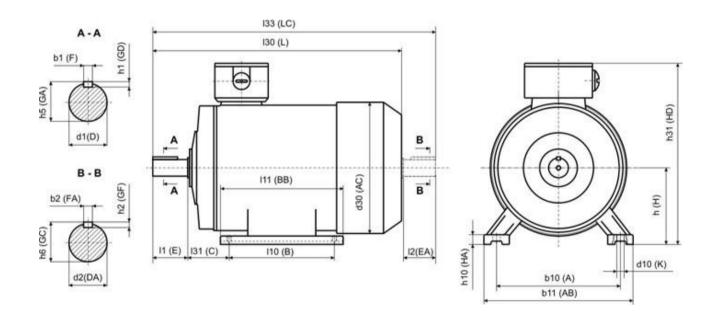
габаритный чертеж электродвигателя исполнение ІМ1081 (1082)
